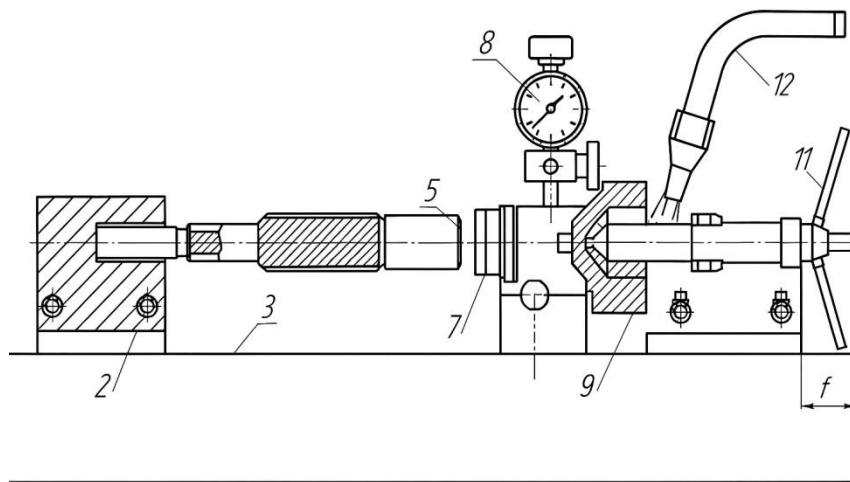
Конструкція пристрою для наплавлення валу-шестірні головної передачі:
